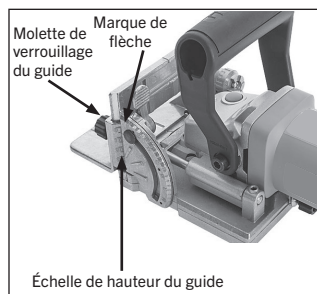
Emplacement des composantes de réglage de la hauteur de coupe.
